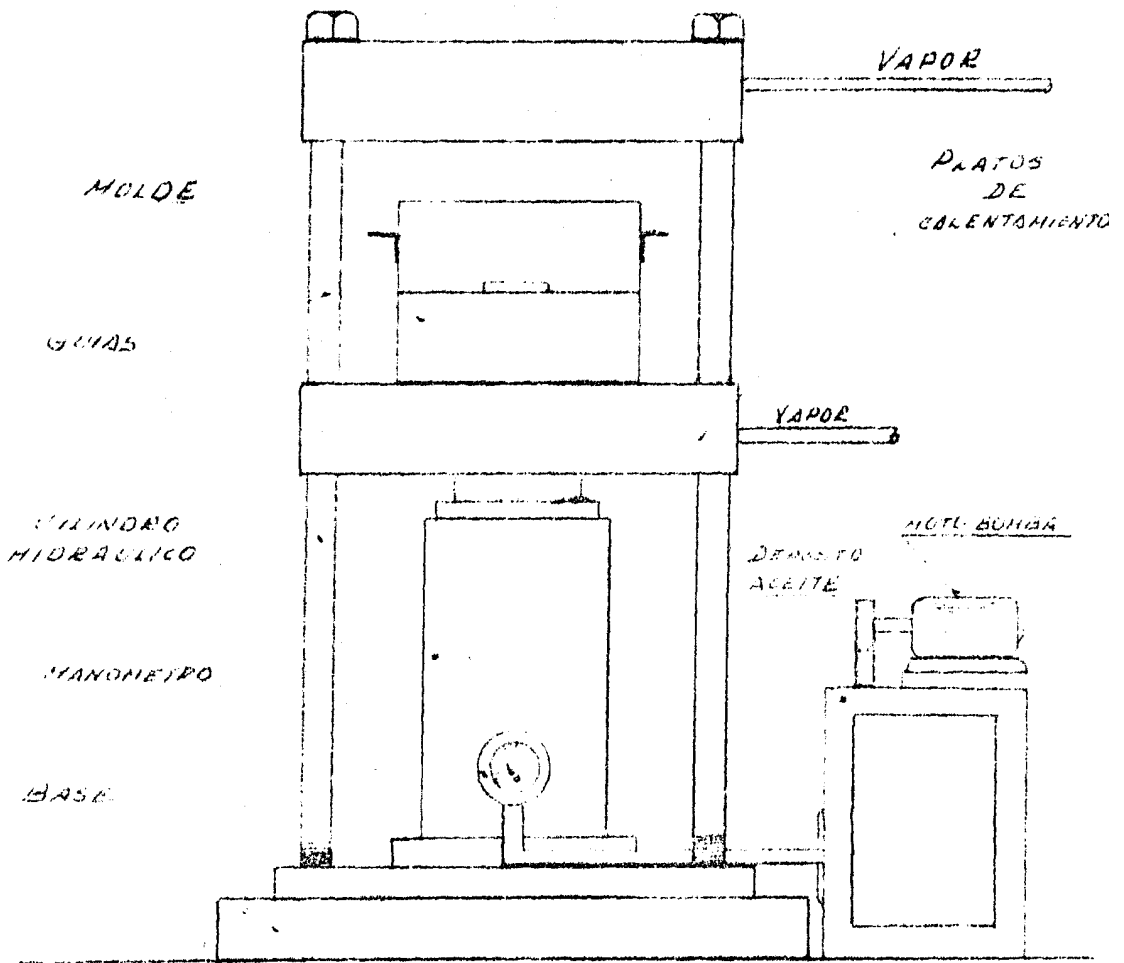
PRENSA HIDRAULICA (VISTA FRONTAL)
